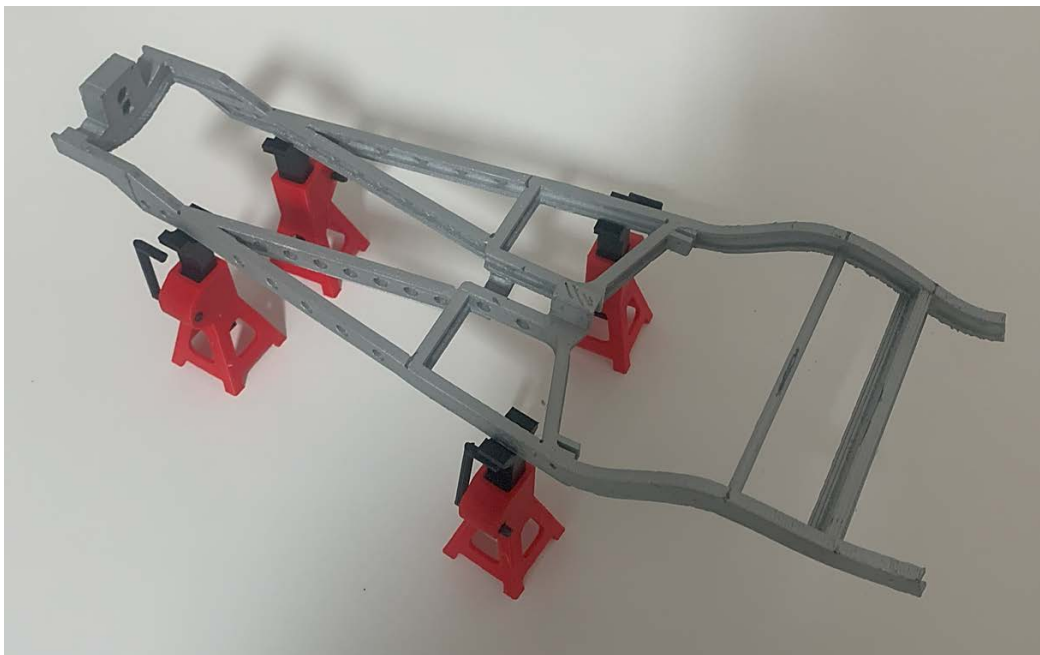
Chassis 1:10 produzido por impressão 3D.
